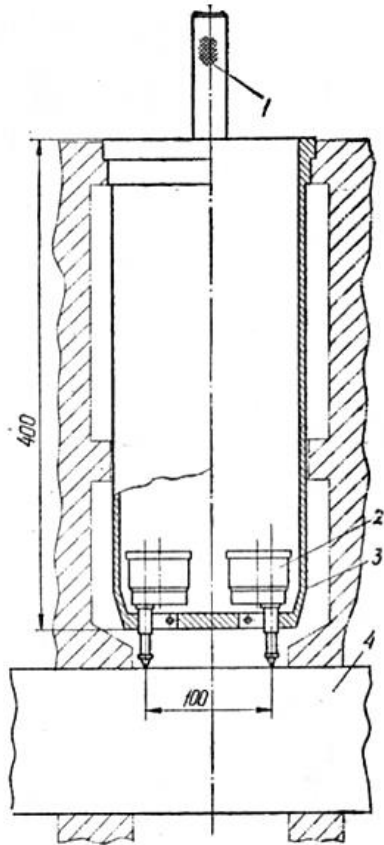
Пристрій для перевірки паралелності опорних поверхон під гільзи до осі колінчатого вала: 1 – рукоятка; 2 – індикатрні головки; 3 – корпус; 4 – оправка
